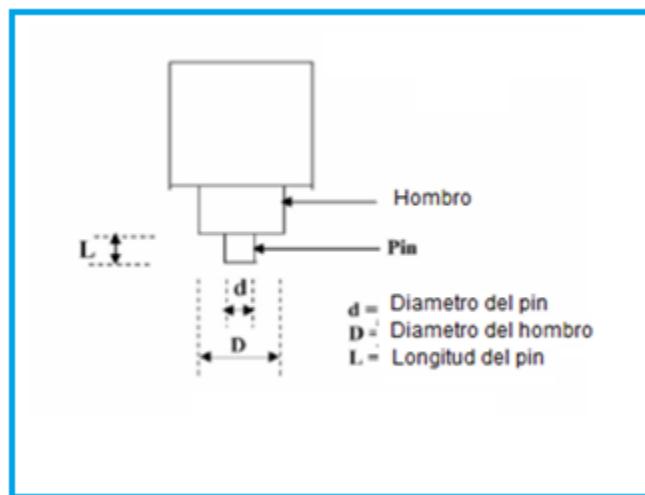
Proceso de soldadura por fricción - agitación.
